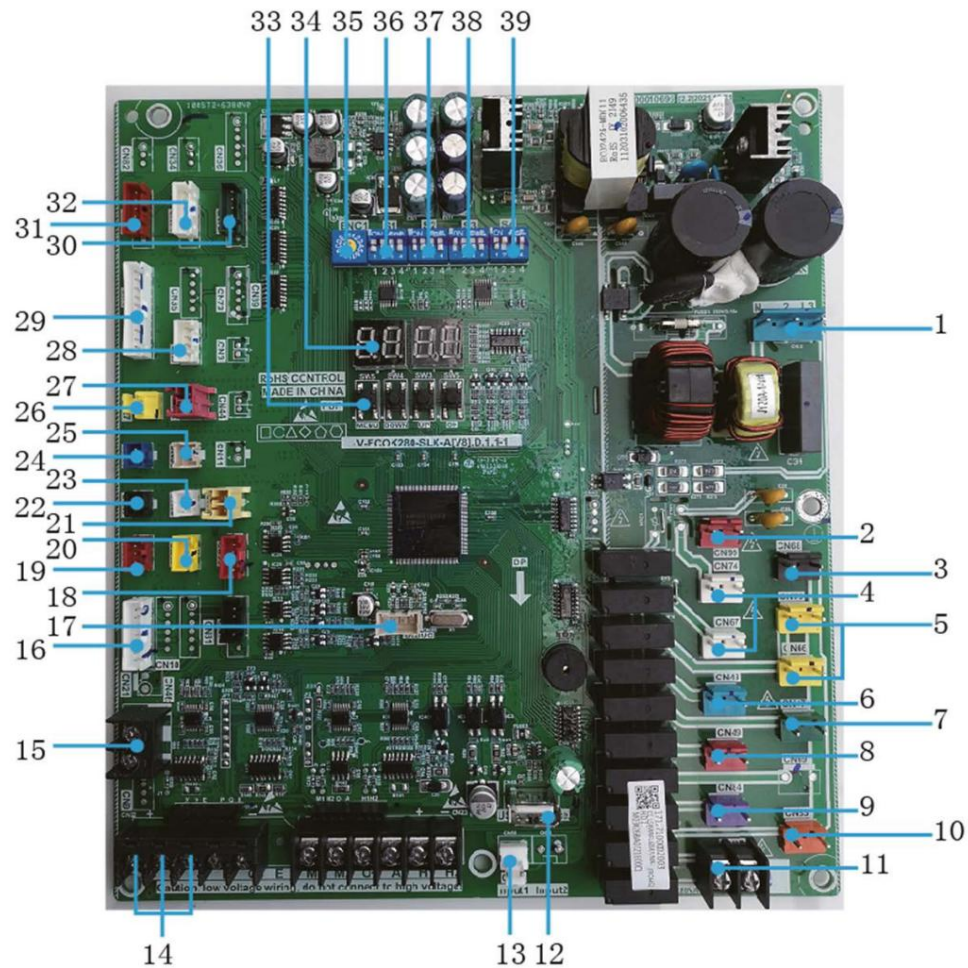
Placa principal de 65KW&75KW&110KW&140KW
